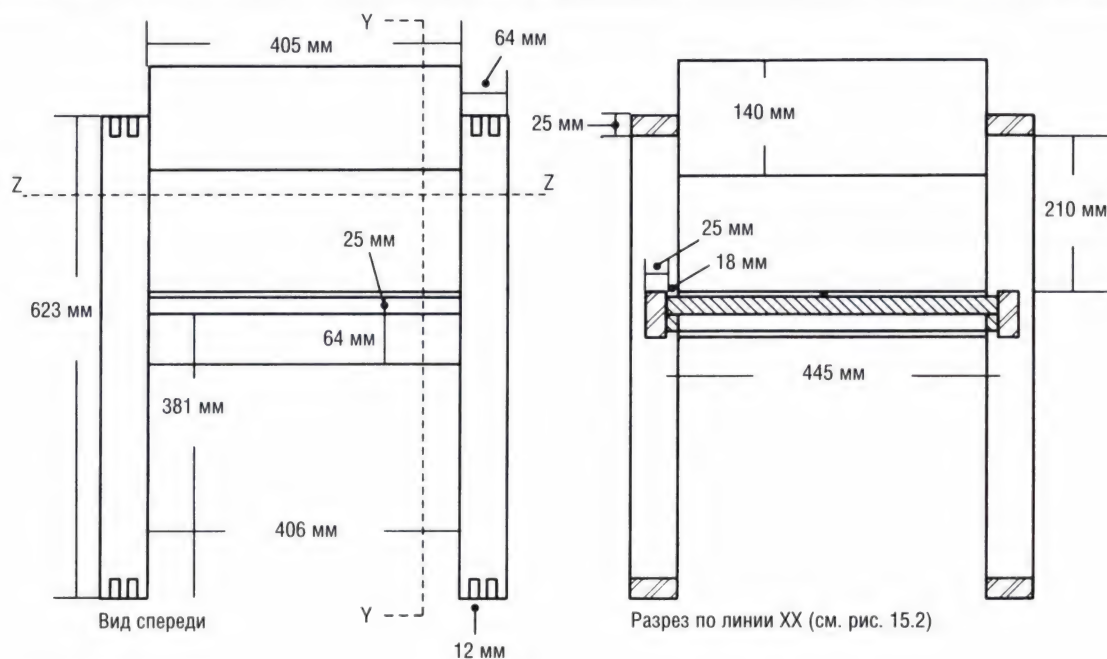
Вид спереди и фронтальный разрез с размерами.
